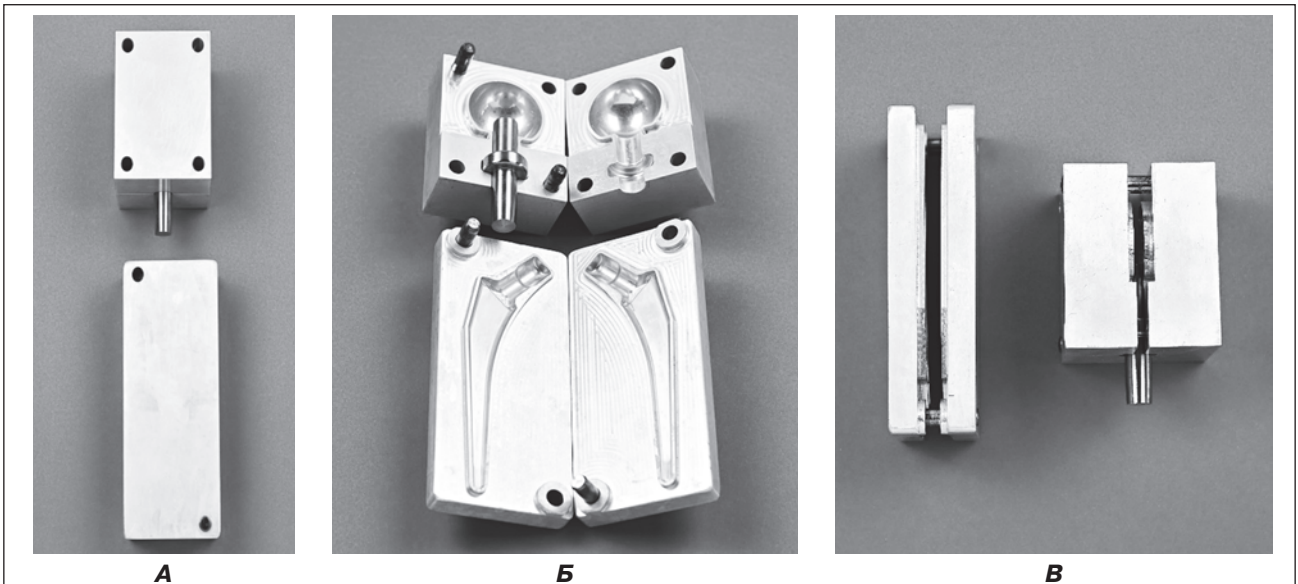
Прес-форма для інтраопераційного виготовлення спейсерів II покоління: А – вигляд зверху; Б – розкладена прес-форма (розмір головки – 50, ніжки – 7,5); В – вигляд збоку
